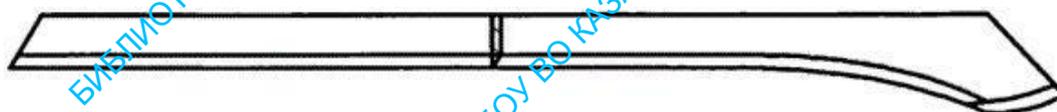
Заготовка в соответствии с формой долотообразного лемеха
